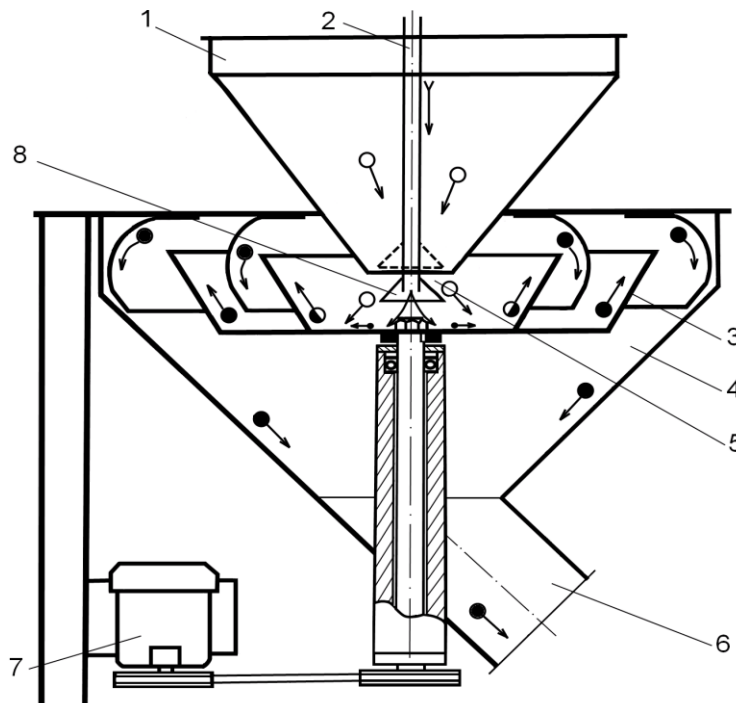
Робочий процес протруювача інерційно-фрикційного типу ПНУ-10 (модифікований): 1 – бункер; 2 – трубка подачі робочої рідини; 3 – чашоподібний змішувач; 4 – камера протруювання; 5 – дозатор насіння; 6 – вивантажувальна горловина; 7 – електродвигун приводу; 8 – конічний розподільник (дозатор).
